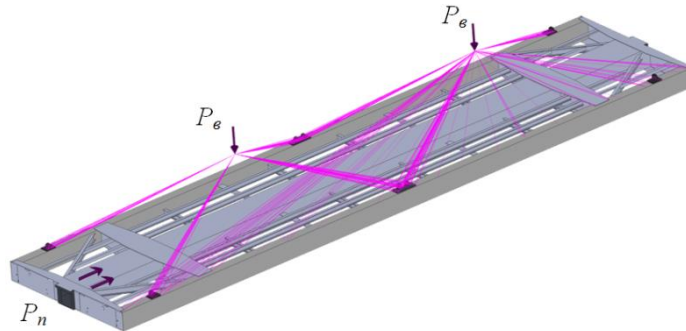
Розрахункова схема несучої конструкції вагона-платформи
